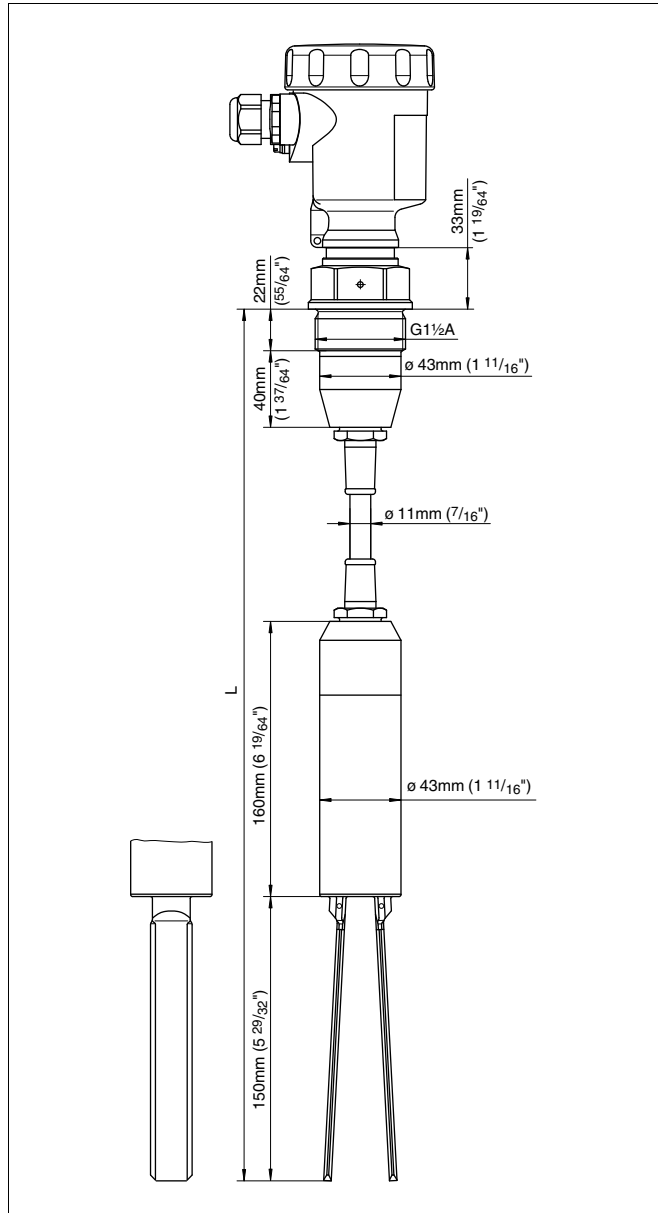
LBV 320 - mit PUR-Tragkabel, Gewindeausführung G1½ A (DIN ISO 228/1)
